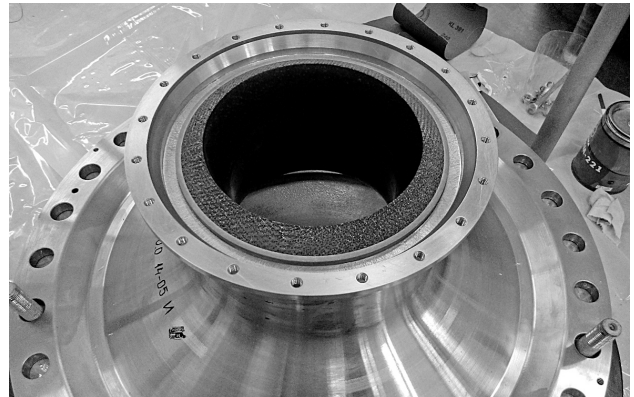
Корпус в сборе перед склейкой с раструбом в сборе
